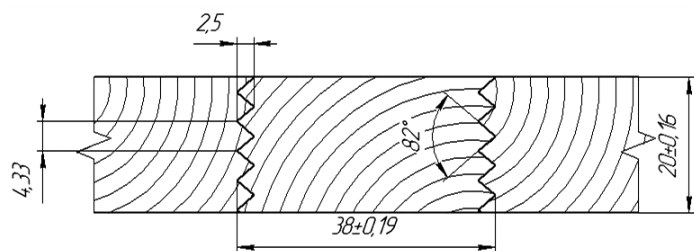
З'єднання ділянок щита за шириною на зубчастий шип
